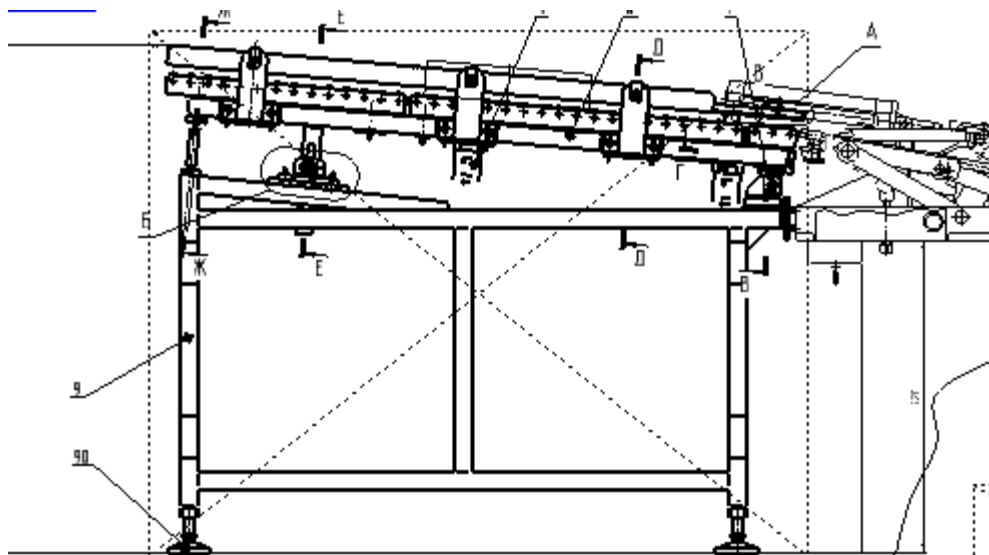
Завантажувач заготовок (вид з іншої сторони)
